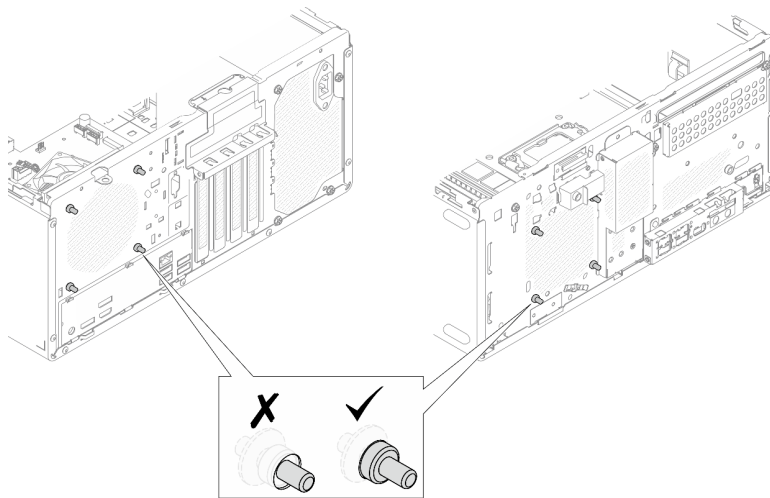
Installation des supports en caoutchouc du ventilateur avant et du ventilateur arrière
